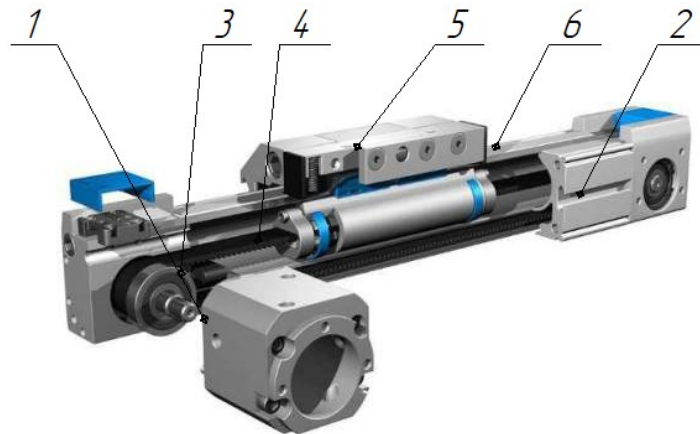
Конструкція «осі»: 1 – вхідний вал; 2 – корпус; 3 – шківів; 4 – зубчастий пас; 5 – каретка; 6 – напрямна каретки.
